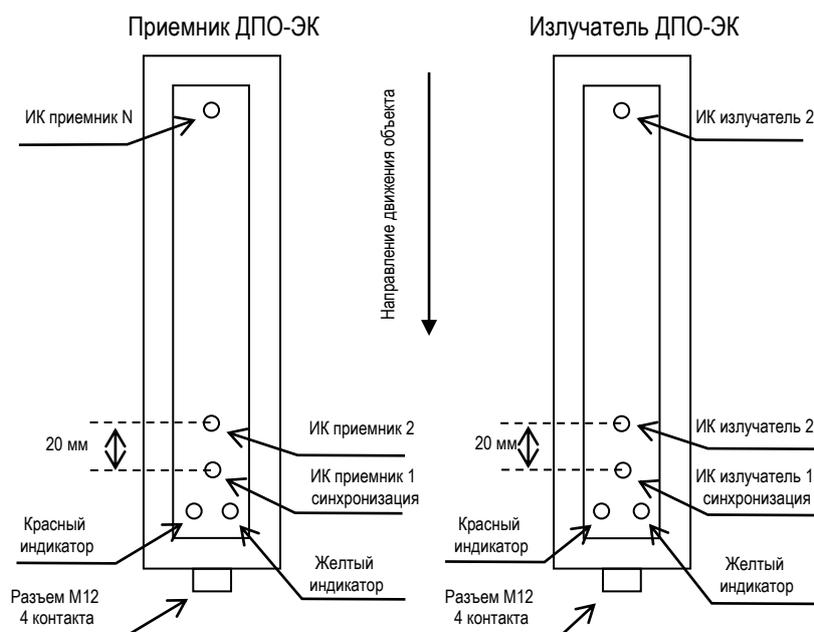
Внешний вид и габаритные размеры ДПО-ЭК20
